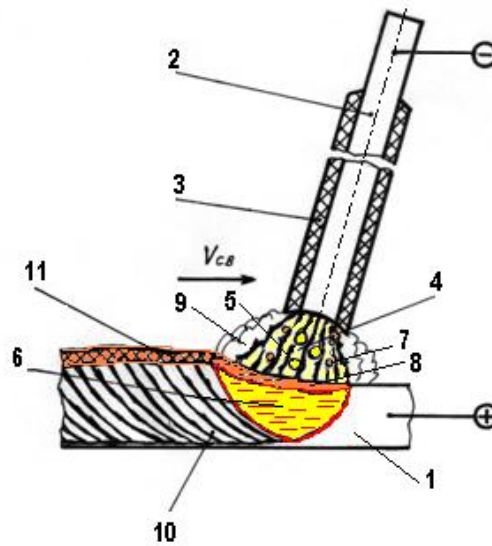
Схема процесса сварки покрытым электродом: 1 – свариваемый металл; 2 – стержень электрода; 3 – покрытие электрода; 4 – дуга; 5 – капли расплавленного металла электрода; 6 – сварочная ванна; 7 – капли плавящегося покрытия; 8 – слой жидкого шлака, образовавшегося из веществ покрытия; 9 – газовая защитная атмосфера (тоже из покрытия); 10 – сварной шов; 11 – шлаковая корка, которая впоследствии счищается
